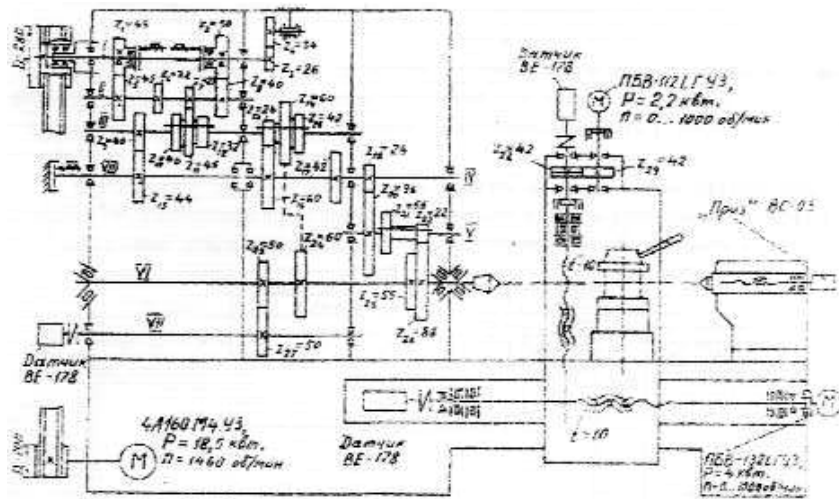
Кинематическая схема токарного патронно-центрового станка 1М63БФ30С1 с ОСУ
